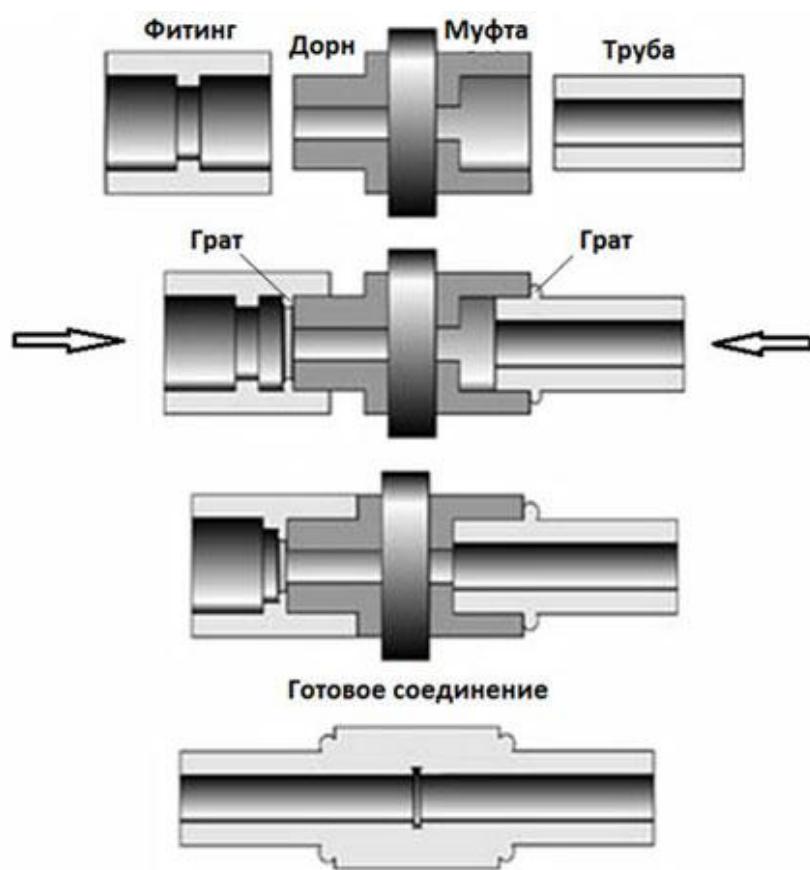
Сварка фитингов с трубопроводом
